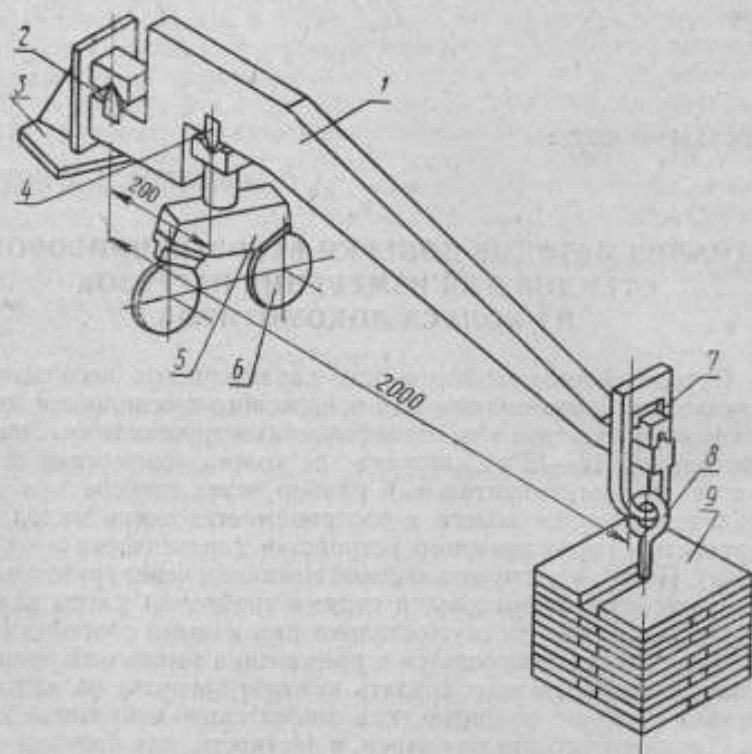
Схема рычажного поверочного устройства типа 74П-20.
